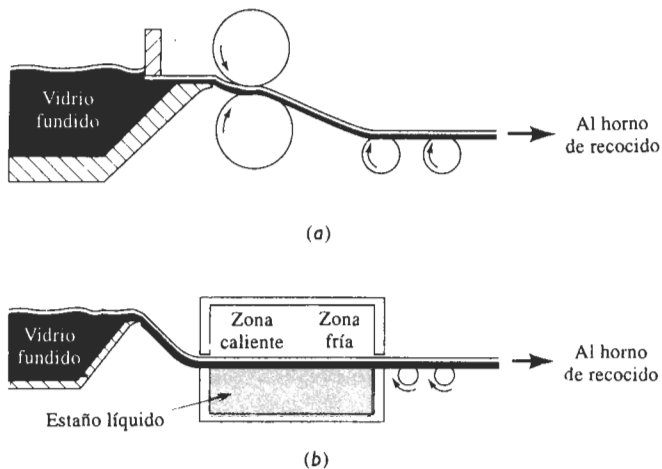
Técnicas para la manufactura de vidrio en hoja y en placa: (a) Laminado y (b) flotado del vidrio sobre estaño fundido.
